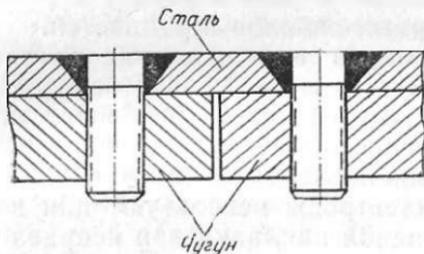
Схема сварки чугуна с использованием стальных пластин
